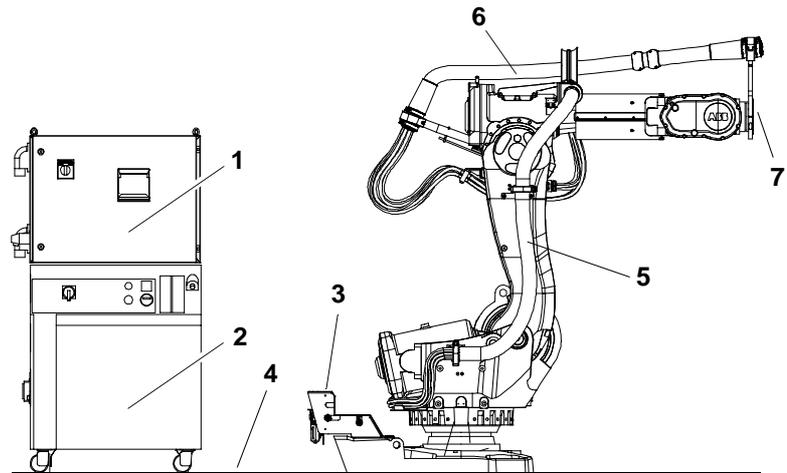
SpotPack type Se pour modules principaux IRB 6600/6650/7600
